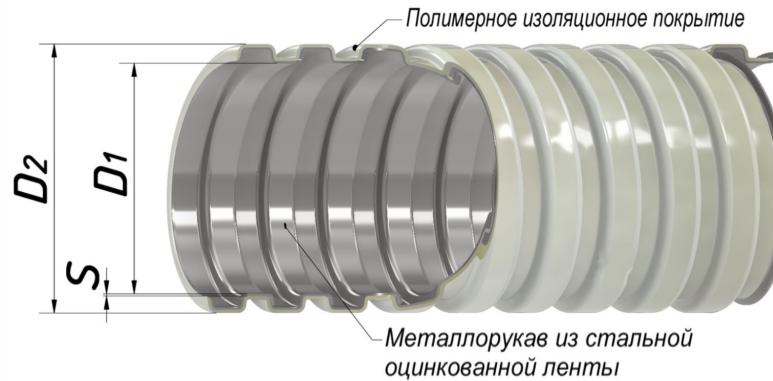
Металлорукав типа РЗ-ЦПнг серый
